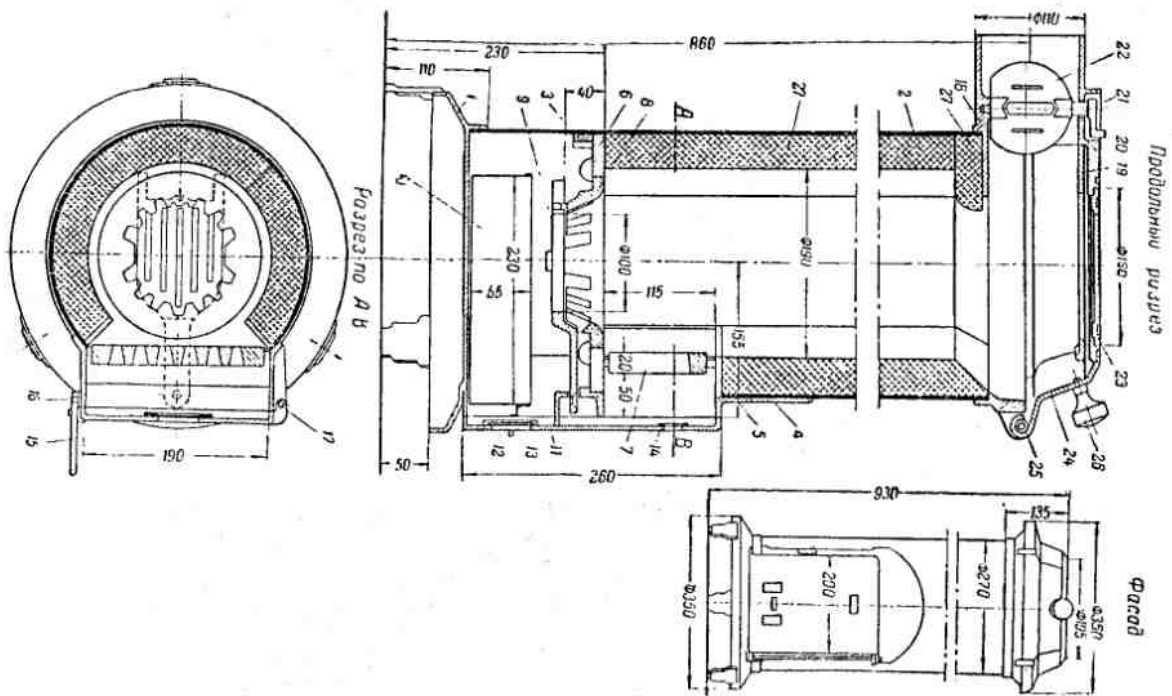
Цилиндрическая печь с футеровкой шамотными вкладышами:
